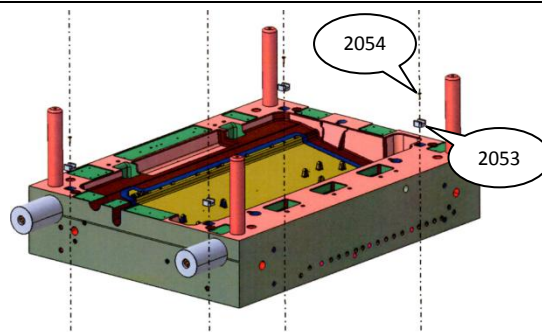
Colocação dos *interlocks* da parte fixa do molde.
